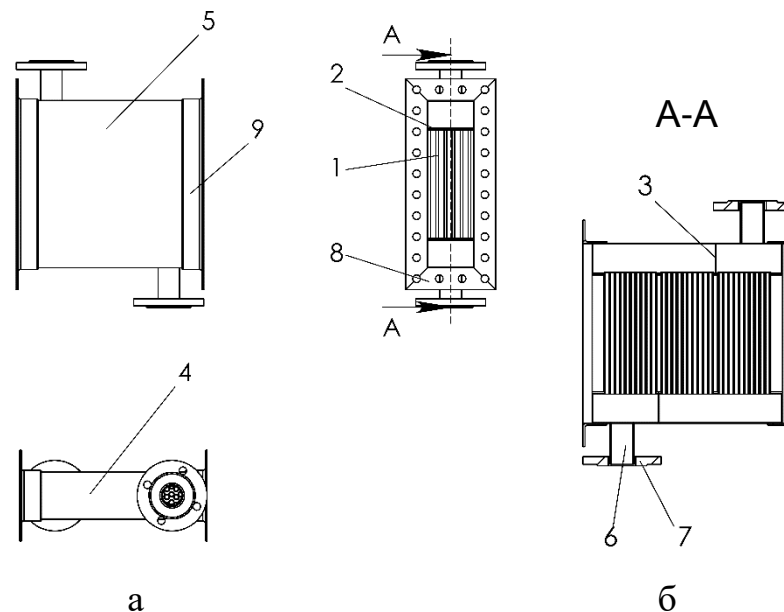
Кожухотрубний теплообмінник: а – загальний вигляд, б – розріз в перерізі А-А
